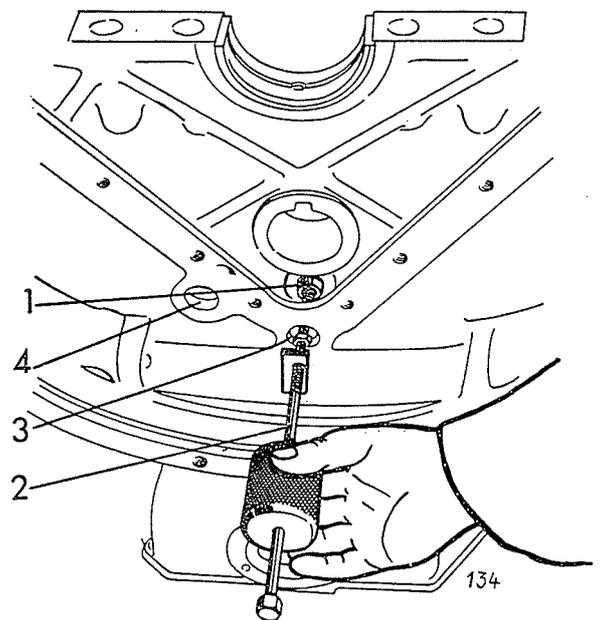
Ausbau der Schmierölleitung für Ventilantrieb F/AL 614
